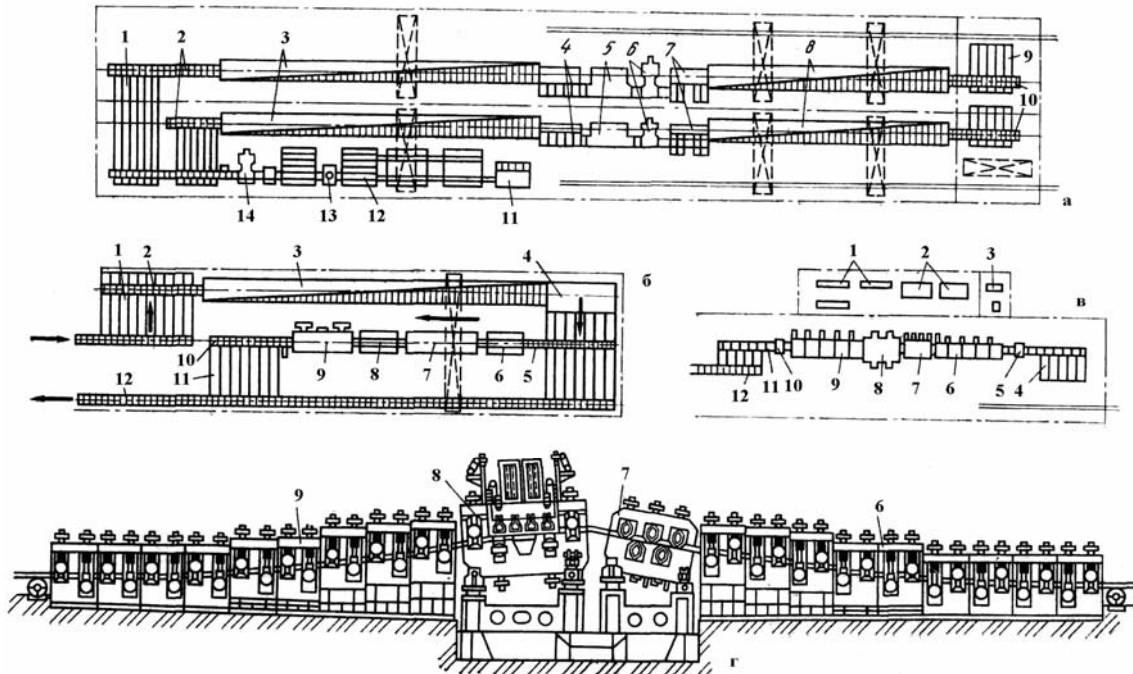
Схема компонувань ділянок для термічної обробки рейок: а – об'ємного гартування в рейкобалковому цеху; б – сорбітизації в рейкобалковому цеху; в – гартування з нагріванням СВЧ; г – поздовжній розріз установки
